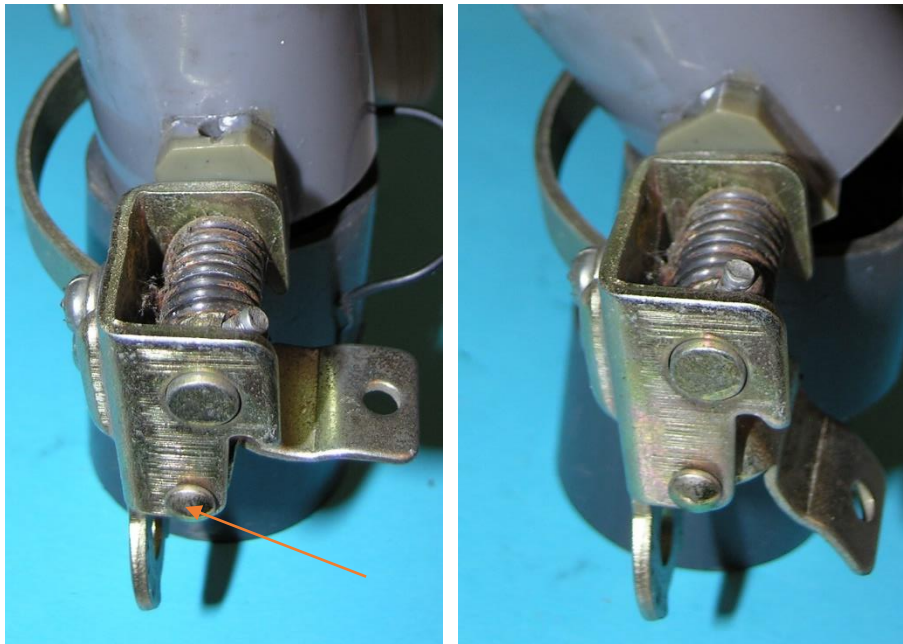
Trennstelle zwischen Drehbolzen und Gehäusemantel: a) Einzelteile, b) Axiale Sicherung mit einer Schraube (Schraube unsichtbar)
